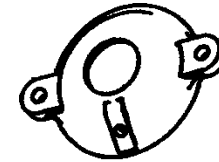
Крышка подшипника КИР.02.0.1001
